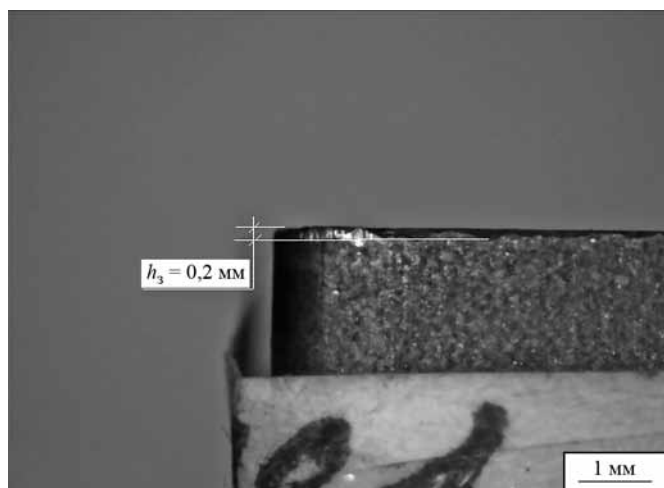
Износ (и разрушение) режущей пластины по задней поверхности
